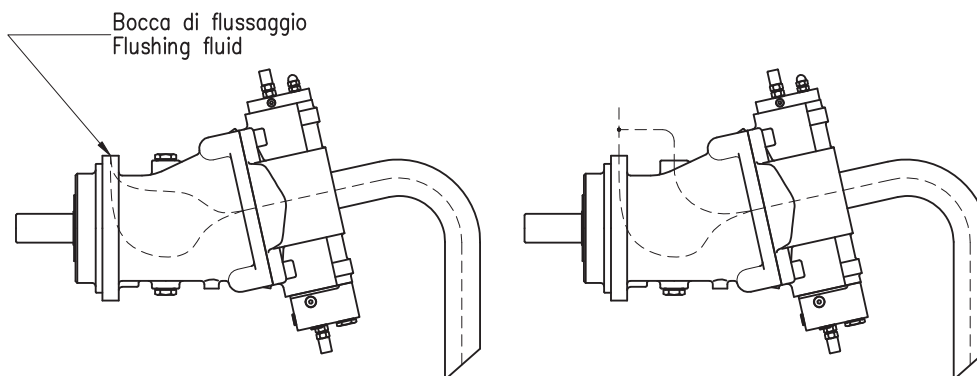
Flussaggio cuscinetti / Figure 4 - Bearings flushing
